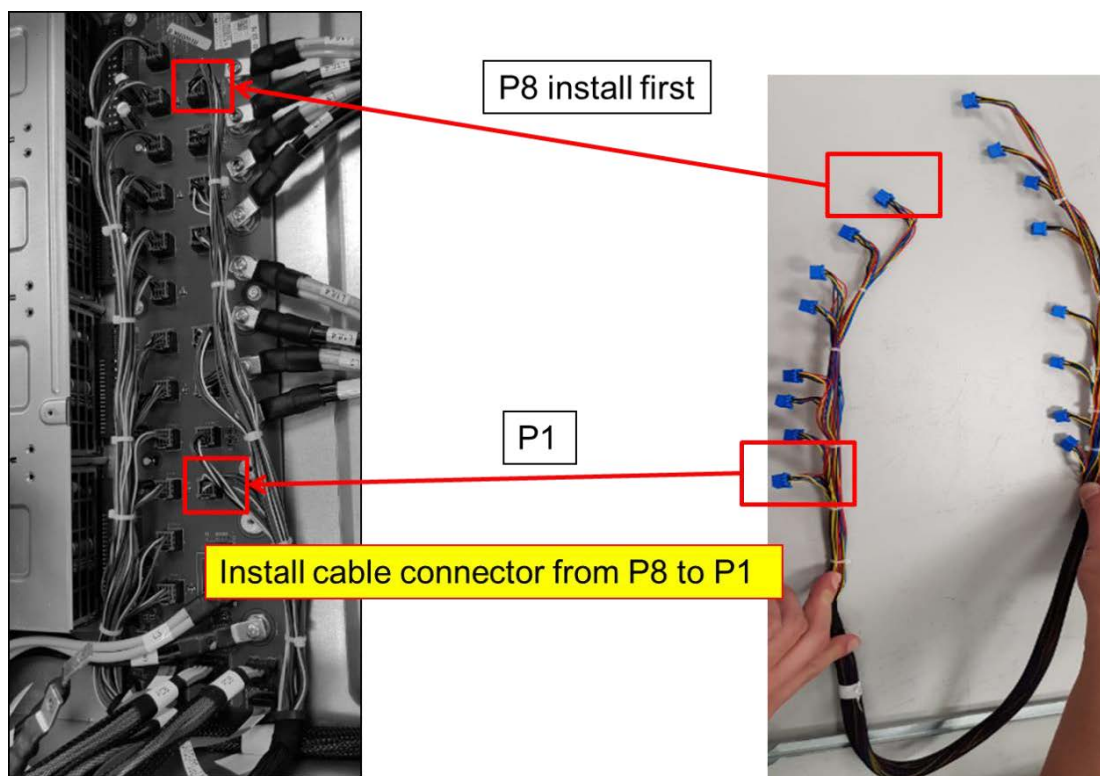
Assemblage du câble de ventilateur MB-PDB vers PDB
